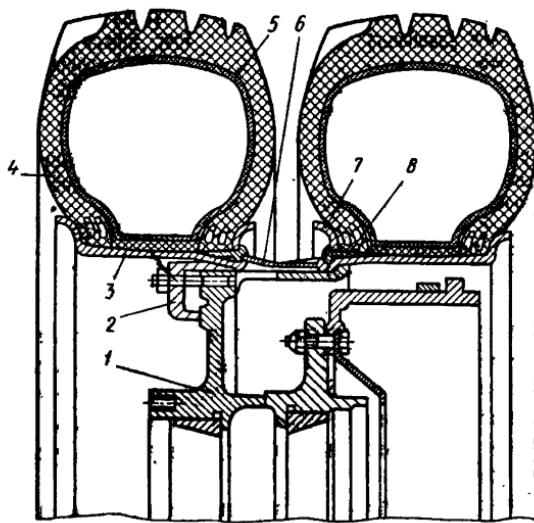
Задние колеса с тормозным барабаном в сборе:
